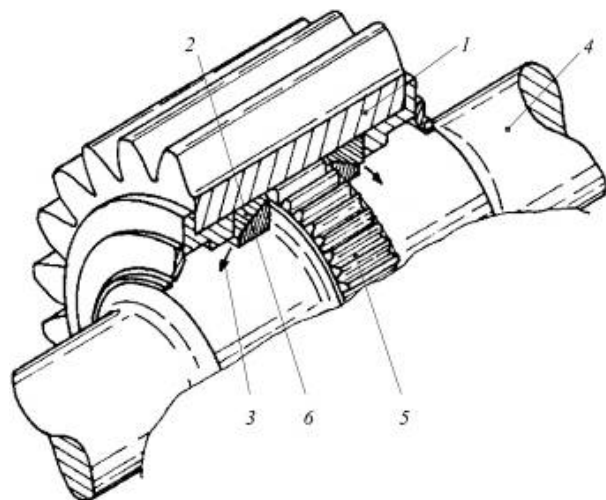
Самоустанавливающееся зубчатое колесо фирмы KruppPolyslus AG: 1 – зубчатый венец шестерни; 2 – внешняя обойма сферического подшипника скольжения; 3 – направление перекоса шестерни к валу; 4 – приводной вал шестерни; 5 – бочкообразная зубчатая передача; 6 – внутреннее кольцо сферического подшипника
